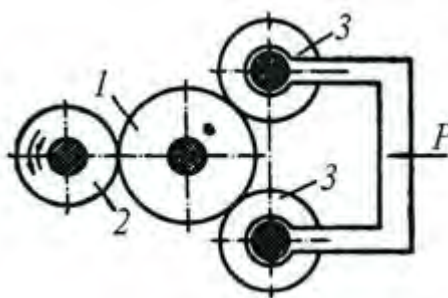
Обкатування зубчастого колеса трьома шестернями-еталонами
